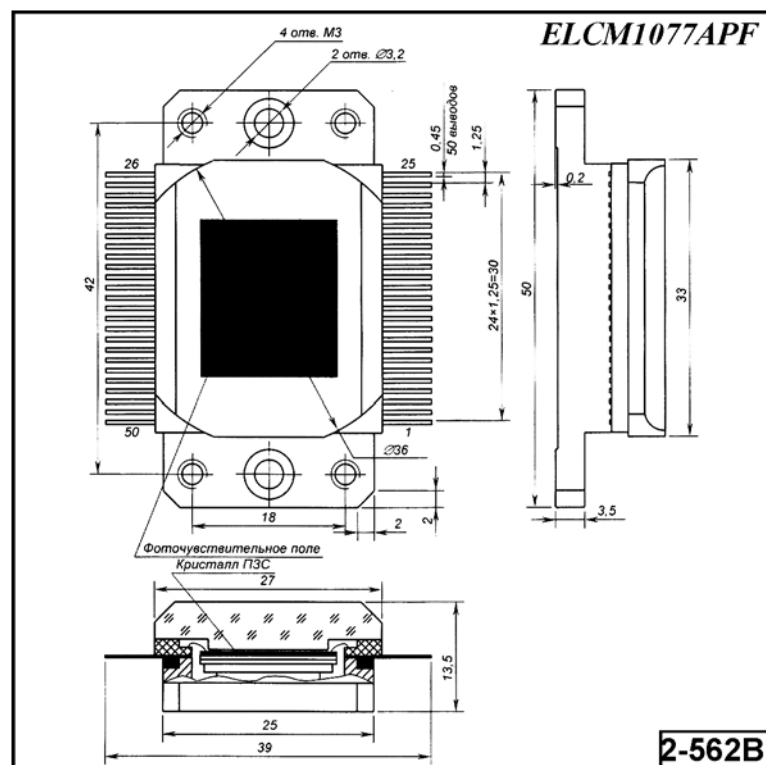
Внешний вид и габаритные размеры ФПЗС ELCM1077APF
